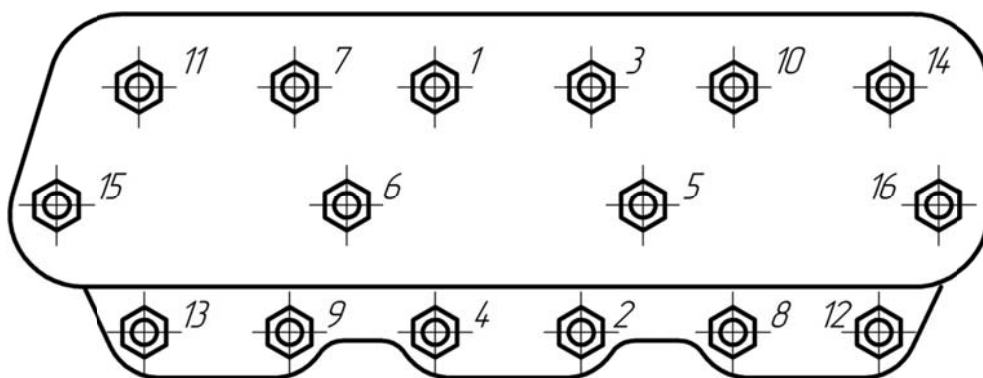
Схема последовательности затяжки гаек крепления головок блока шестицилиндрового двигателя
